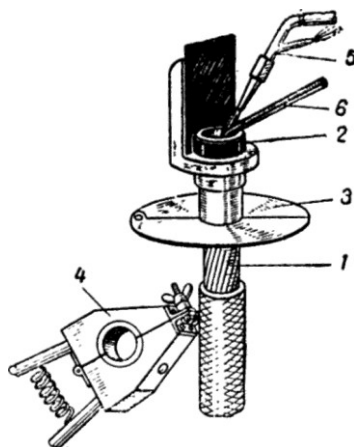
Оконцевание многопроволочной алюминиевой жилы алюминиевым наконечником с помощью газовой сварки. 1 — жила; 2—форма-экран; 3 — защитный экран; 4—охладитель; 5—горелка; 6 —присадочный алюминиевый пруток.
